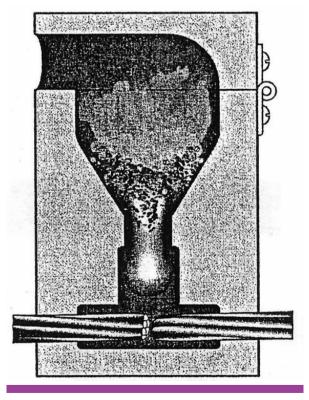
Colada del material fundido sobre las piezas a soldarse
